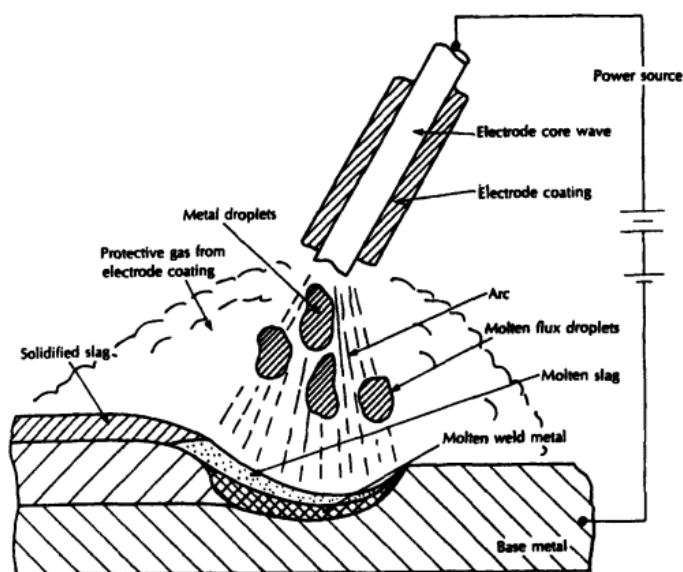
Esquema del proceso SMAW, que incluye: el porta electrodo y el electrodo, la soldadura y la conexión eléctrica
